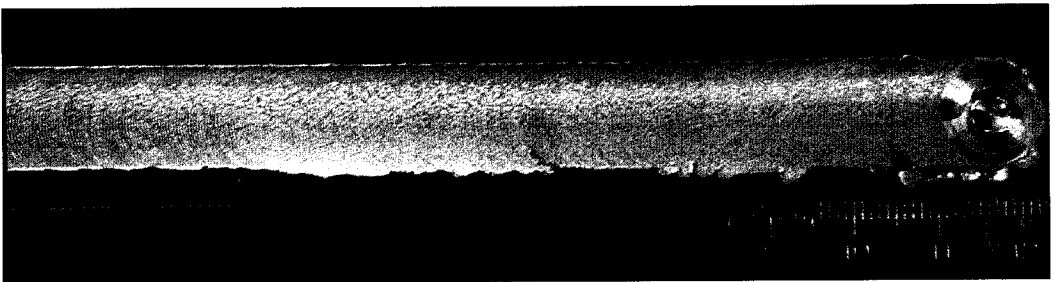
Vista da superfície da chapa soldada pelo processo de *Friction Stir Welding*.
